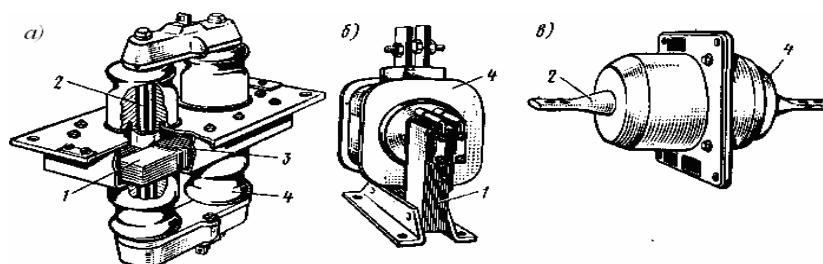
Прохідний багатовитковий - ТПЛ (а), котушковий - ТКФ-3 (б) і прохідний одновитковий - ТПОЛ-10 (в) трансформатори струму: 1 - осердя; 2 - первинна обмотка; 3 - вторинна обмотка; 4 - фарфорова підстава (або литий корпус)
